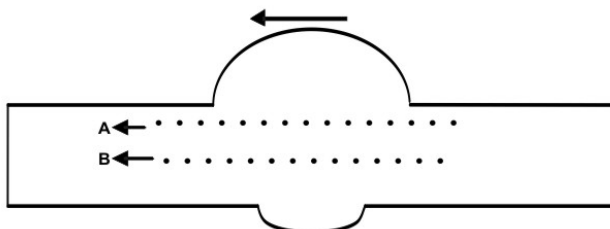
Esquema de barrido de durezas sobre la probeta soldada.
